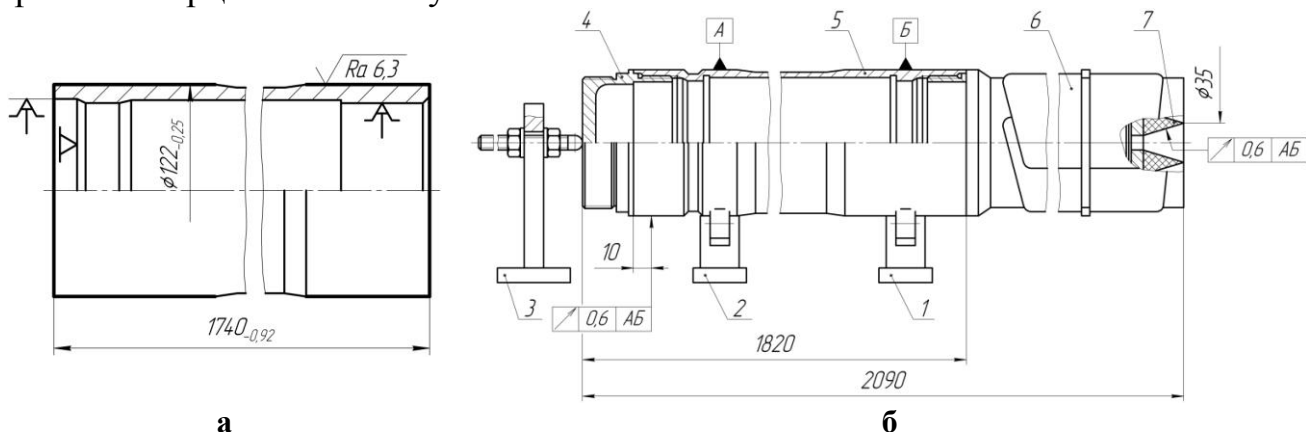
а) операционный эскиз и схема базирования на операции чистового точения центрирующих утолщений, совмещенного с подрезкой торцов; б) схема контроля биения собранного узла
